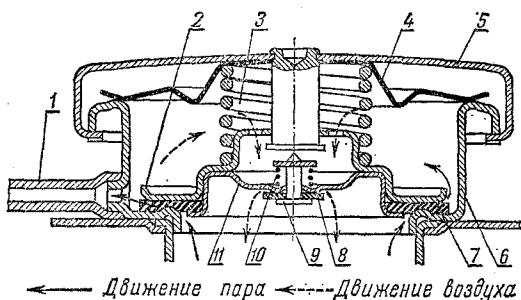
Крышка горловины радиатора с паровым и воздушным клапанами (двигатель ГАЗ-53):
